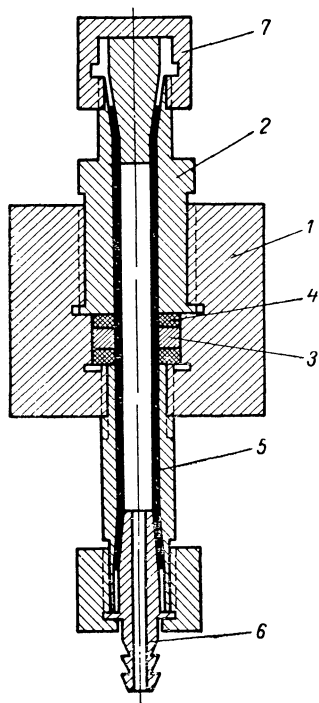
Приспособление для сжатия кольцевых ферритовых сердечников давлением по внешней цилиндрической поверхности.
